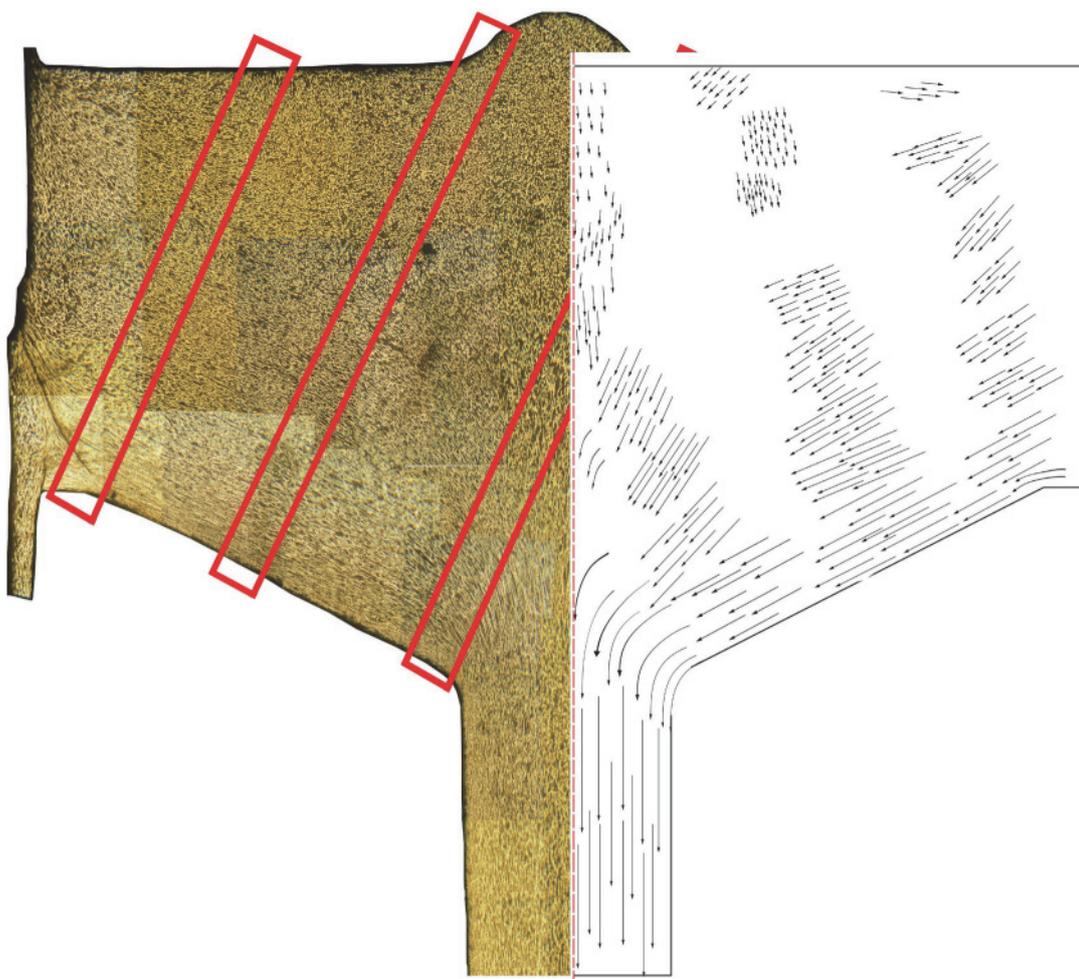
Поле деформаций твердых частиц при прямом прессовании тиксозаготовки из сплава АК7
